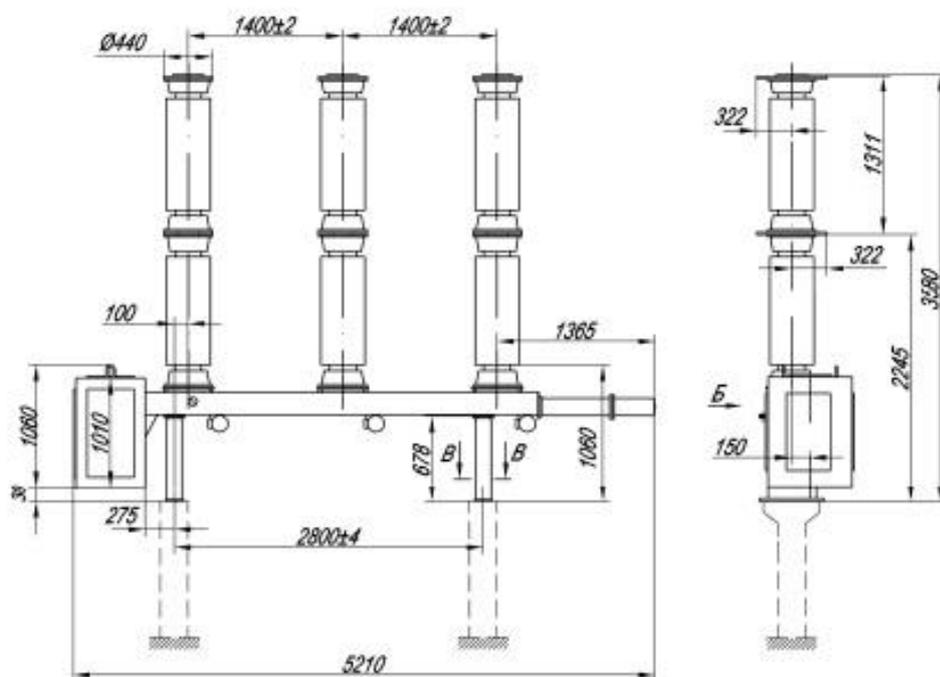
Внешний вид и габаритные размеры выключателя ВГТ-110П-40/2500 У1
